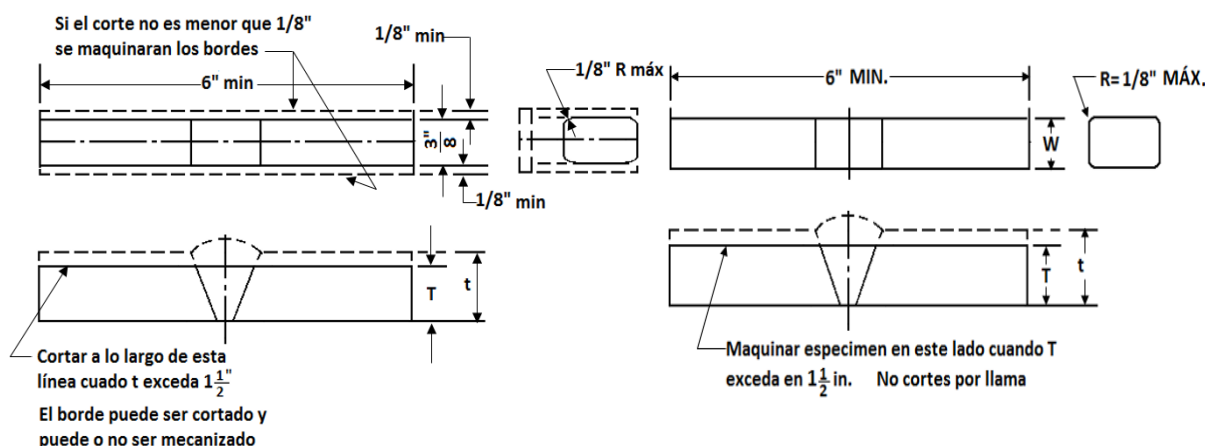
Especímenes placas soldadas de lado según ASTM E190
